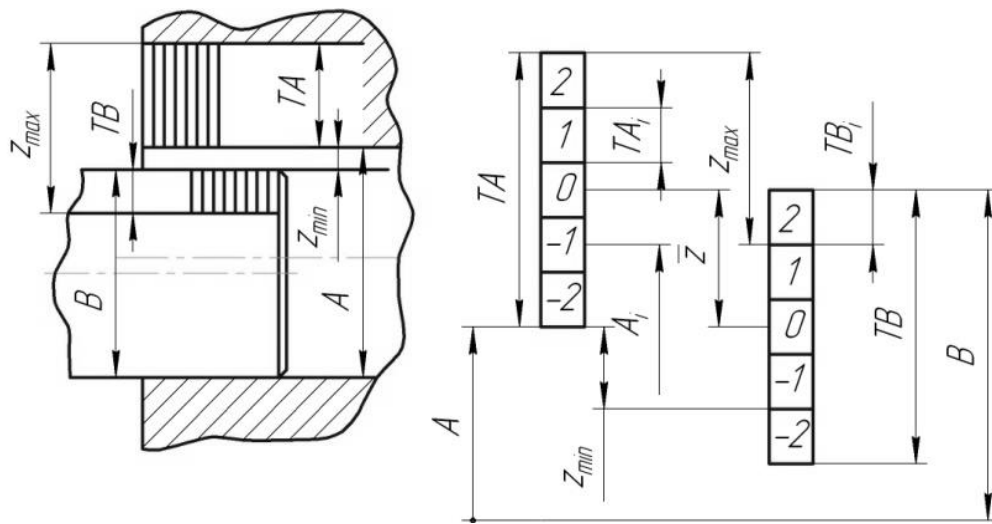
Схемы соединения вала с втулкой и разбивки допусков размеров на группы
